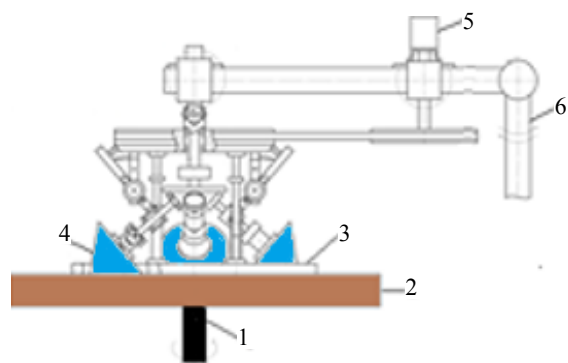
Схема устройства: 1 – шпиндель базового станка, 2 – инструмент-планшайба, 3 – правильник в виде стеклянной пластины с отверстиями для деталей, 4 – деталь (плоско-выпуклая коническая линза), 5 – привод вращательного движения деталей, 6 – вал привода возвратно-вращательного движения деталей
